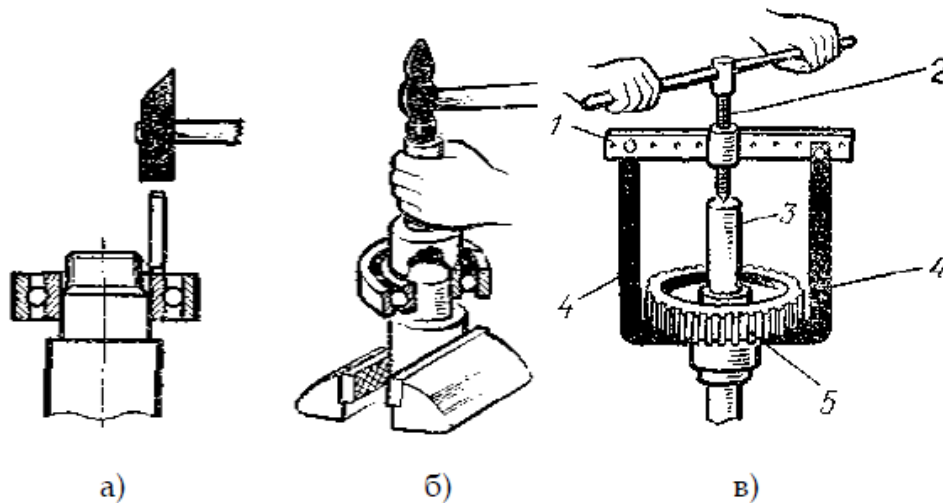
пристосування для складальних робіт: а – виколотка; б – оправка; в – гвинтовий знімач; 1 – опора; 2 – гвинт; 3 – вал; 4 – лапи; 5 – деталь, що знімається
